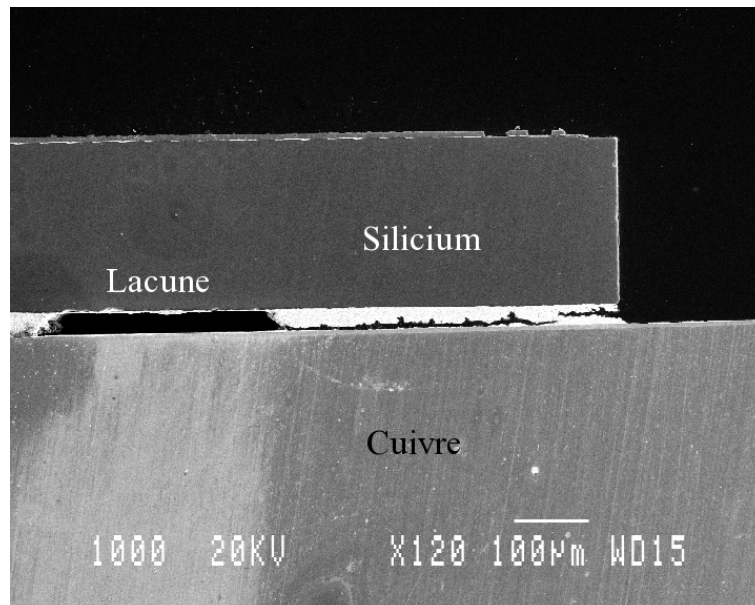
Fissure dans l’assemblage C6\_03 T2
